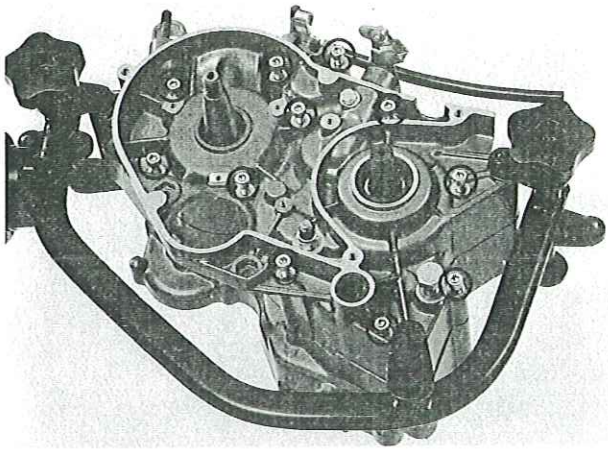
Tambor desmodrómico y grupo engranajes cambio
